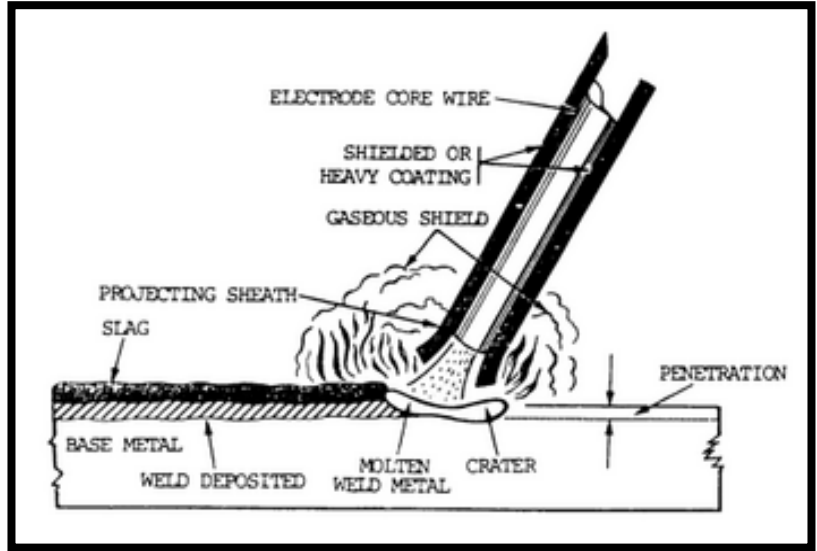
en la izquierda: Obrero soldador haciendo uso del arco eléctrico para la realización de la soldadura en una pieza. Imagen 124 a la izquierda: Esquema grafico que muestra el proceso detallado de la soldadura mediante la utilización de arco eléctrico. Estas eran algunas de las actividades que se realizaban en la planta No. 2, producto del proceso de modernización que sufrió la empresa tras la fusión en 1960 con Falk Corp. (Fuente: acerera.com)
